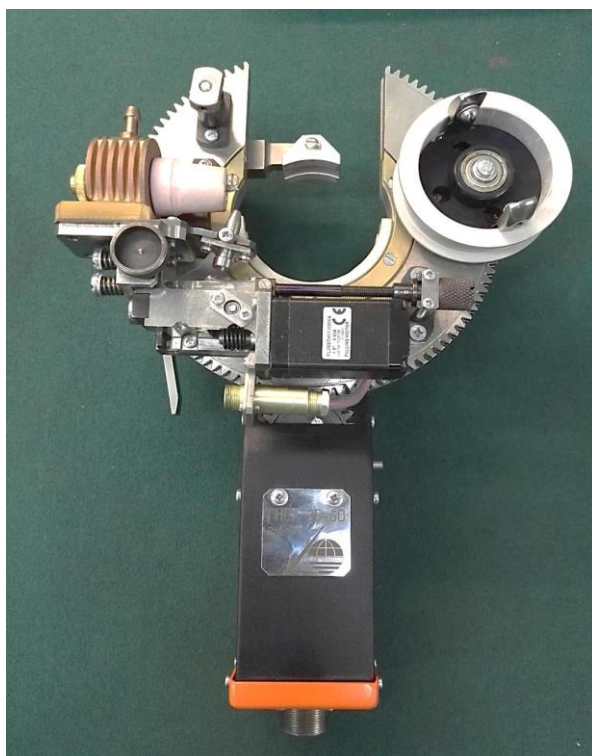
Фото изготовленной сварочной головки ГНСА 25-60
